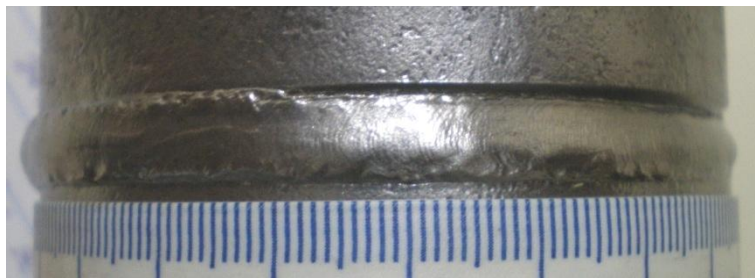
Ensaio com desvio do cordão soldado na descendente.
